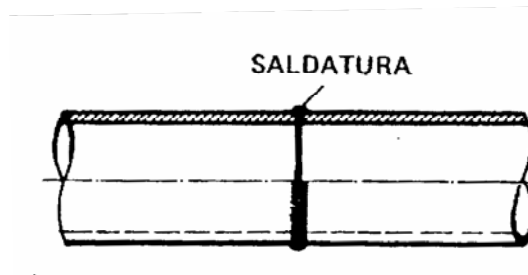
giunzione mediante saldatura (giunto saldato)
